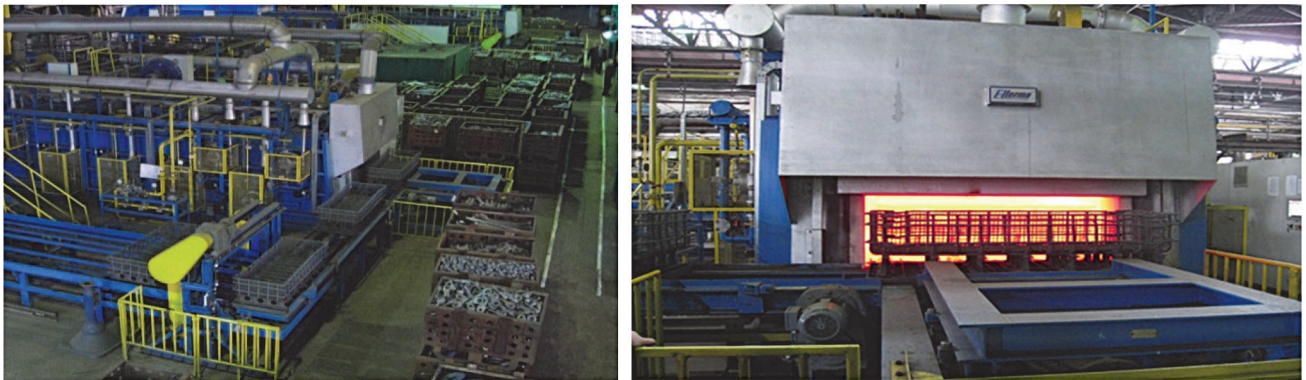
Газовый толкательный агрегат мод. APN-1500G
